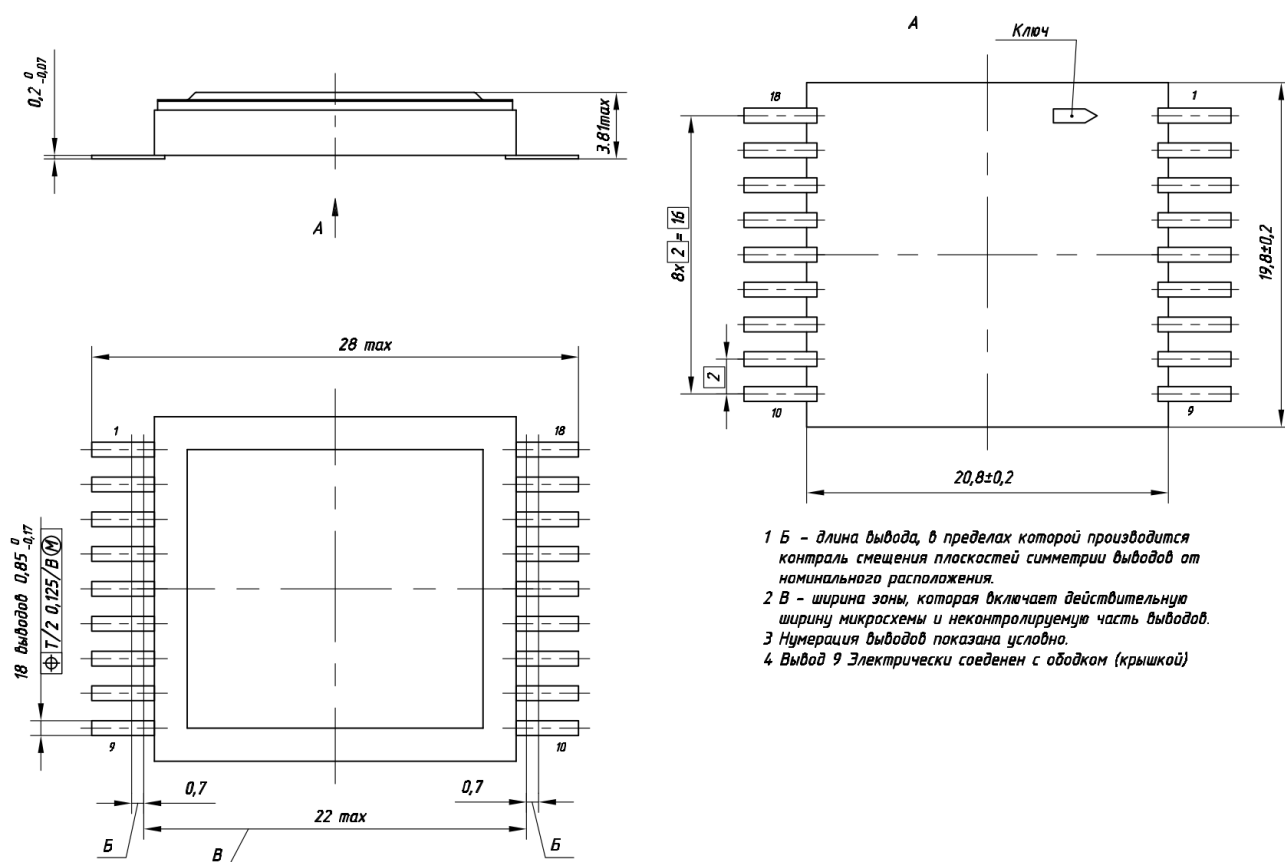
Габаритный чертеж корпуса "5226.18-1"
